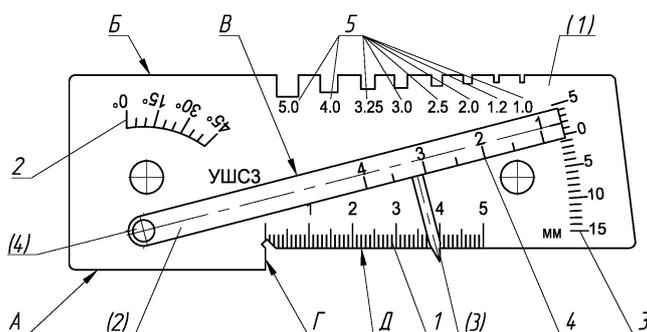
Универсальный шаблон сварщика УШС-3.
